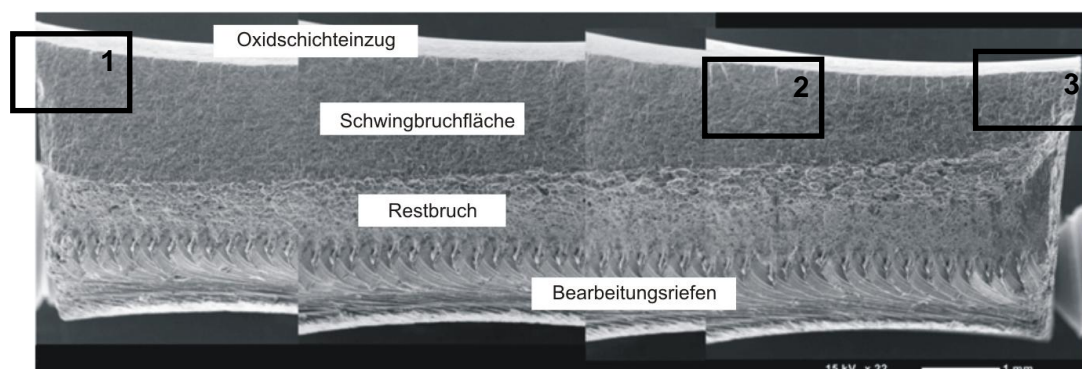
Übersichtsaufnahme der Bruchoberfläche einer Schweißung des Parametersatzes IMWF-11-00001 ($n=750 \text{ min}^{-1}$, $v_x=250 \text{ mm/min}$)
